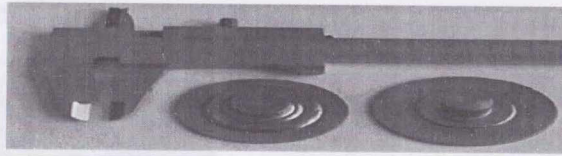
Деталі заготовок мілкомодульних шестерень.
